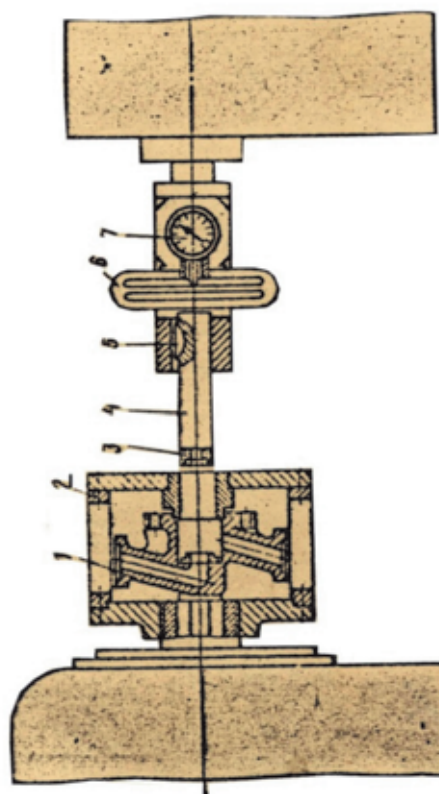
Приспособление для обработки уплотнительных поверхностей
